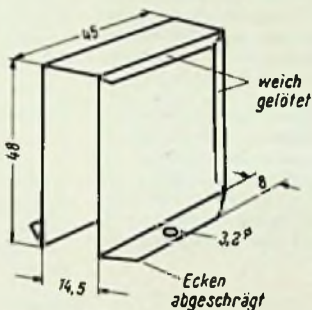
Halterung für Batterieersatz; Material: Weißblock 0,2 mm, die Hauptmaße sind Innenmaße
